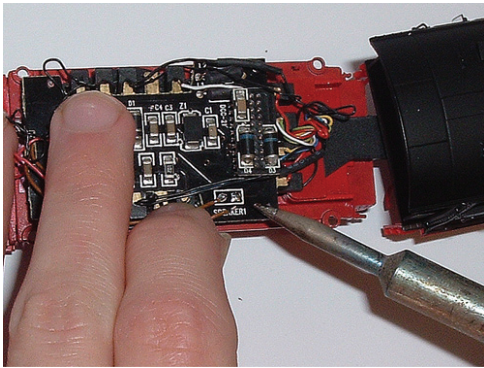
Lautsprecherverlötung / Soldering speaker wires
